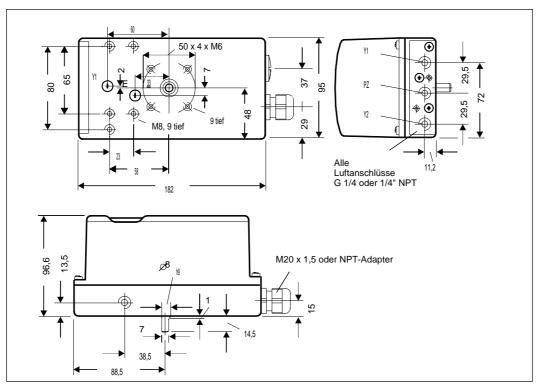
Maßbild Ausführung Kunststoffgehäuse
